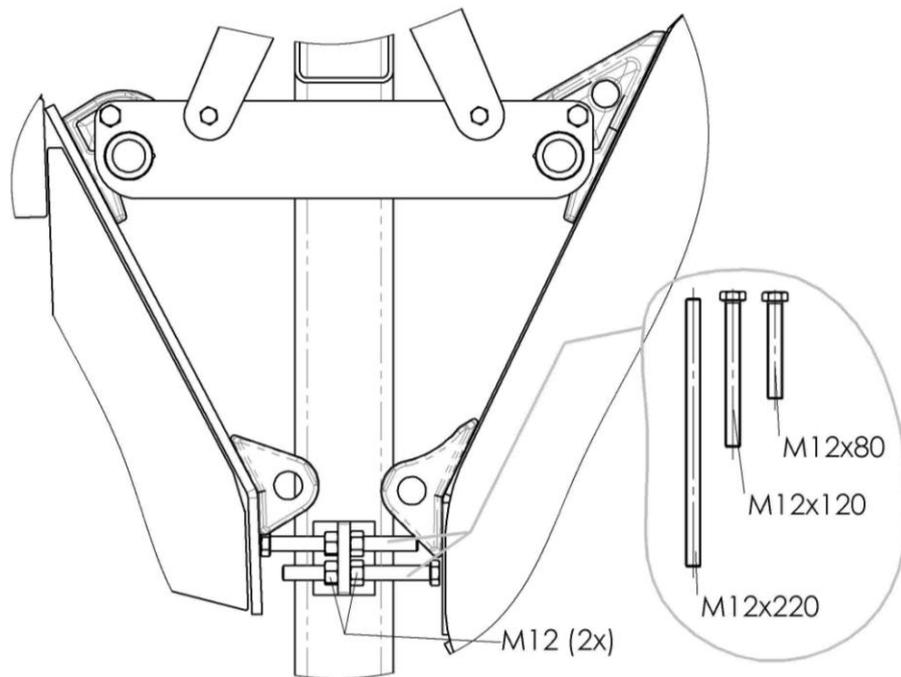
Einstellung der Werkzeugneigung durch Schraubenschlag
